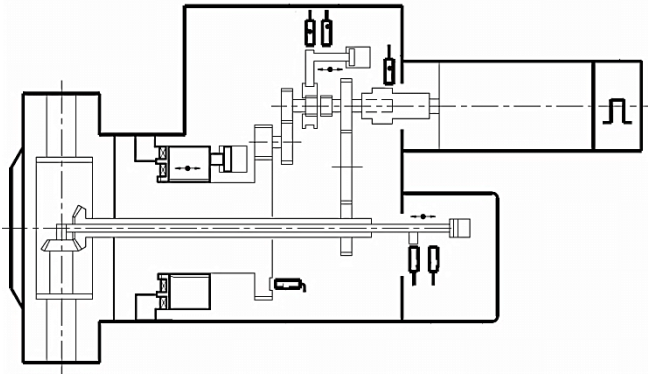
Револьверна головка з одним електродвигуном для повороту інструментального диска та приводу інструмента
